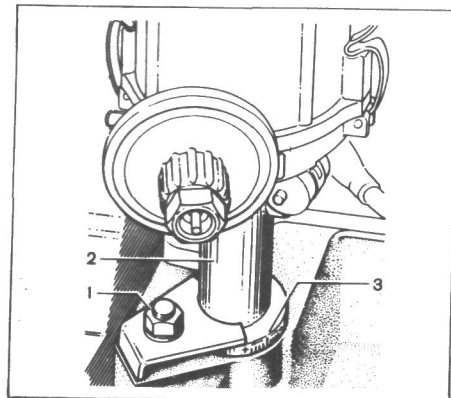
Октан-корректор: 1 — гайка; 2 — корпус распределителя зажигания; 3 — шкала
